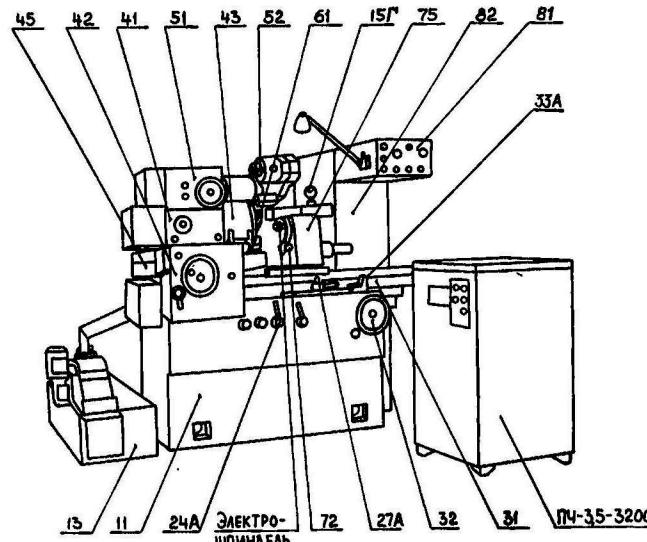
Общий вид станка модели ЗК225А с обозначением узлов
